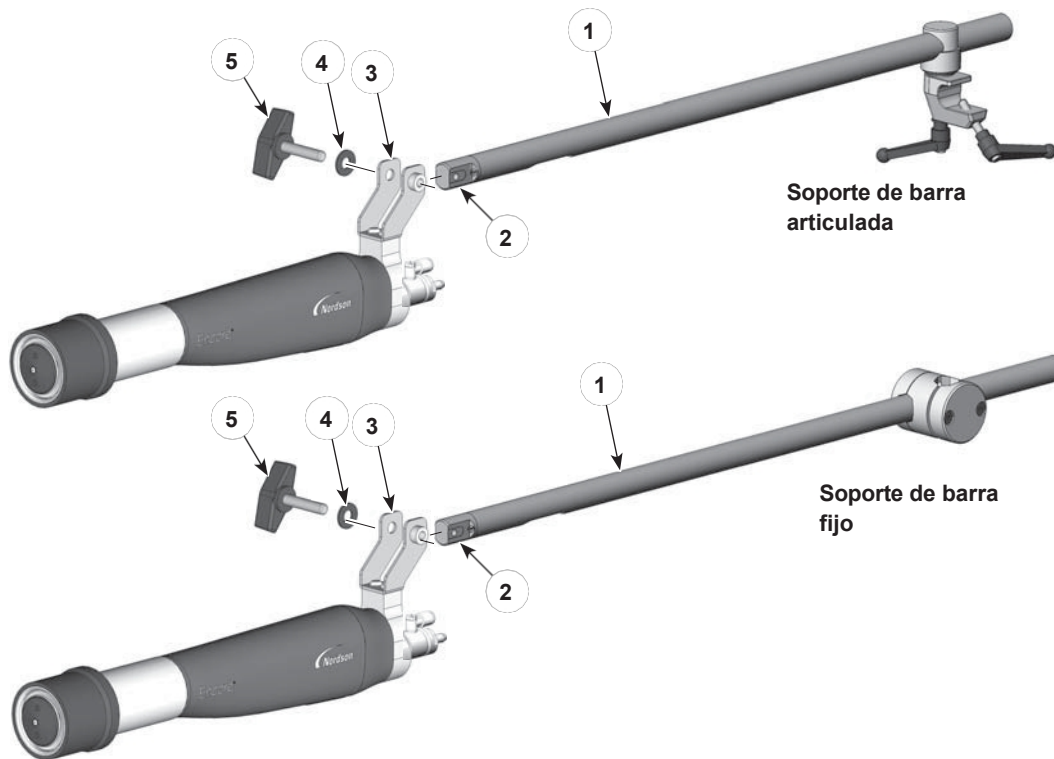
Kits opcionales de montaje de pistola pulverizadora en barra ()
